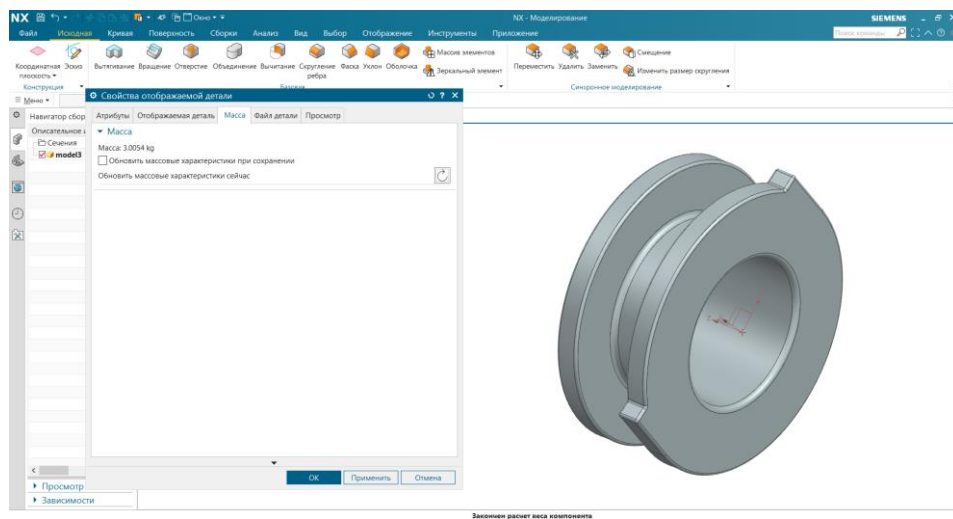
3D-модель заготовки, що отримується литтям у кокіль
